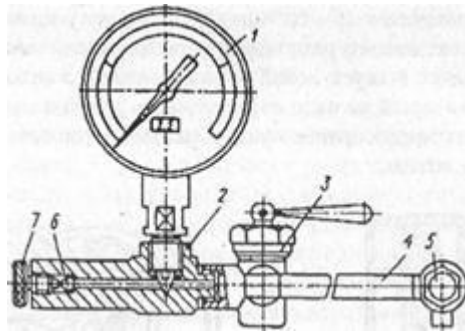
Прибор КИ-4801 для замера давления в системе топливо-подачи низкого давления перед ТНВД: 1 -- манометр; 2 -- переходник; 3 -- кран; 4 -- топливопровод; 5 -- соединительный штуцер; 6 -- шарик; 7 -- винт.
